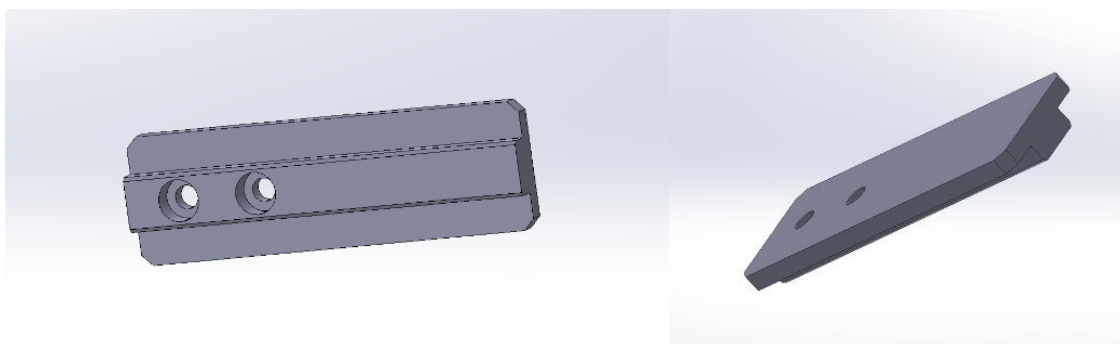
pièces de guidage et de blocage (en bleu).
